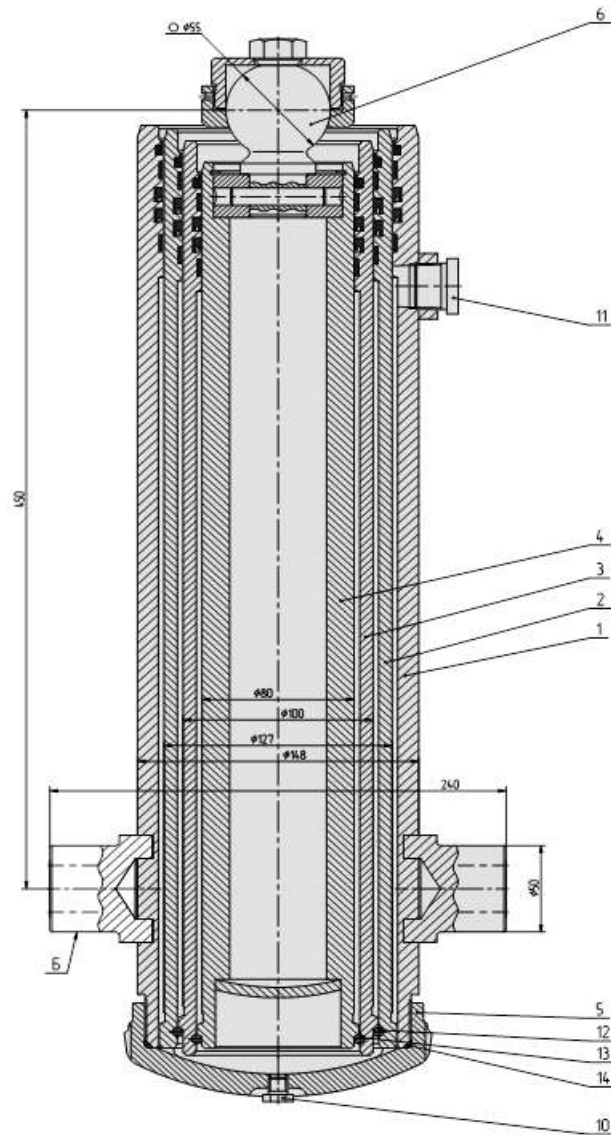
Ескіз гідроциліндра 503А-8603510
